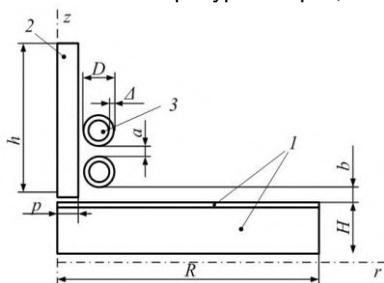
Геометрия модели индукционной точечной сварки: 1 – свариваемые части изделия; 2 – ферритовый стержень; 3 – индуктор
